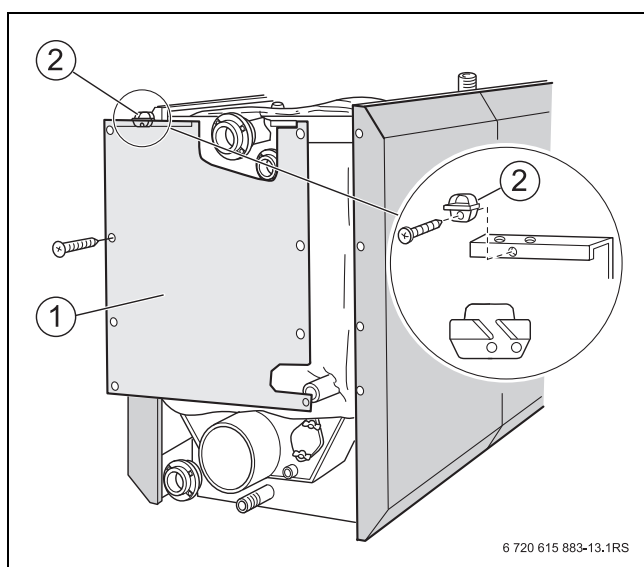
Visser le panneau arrière (taille de chaudière de 400 à 640 kW)
